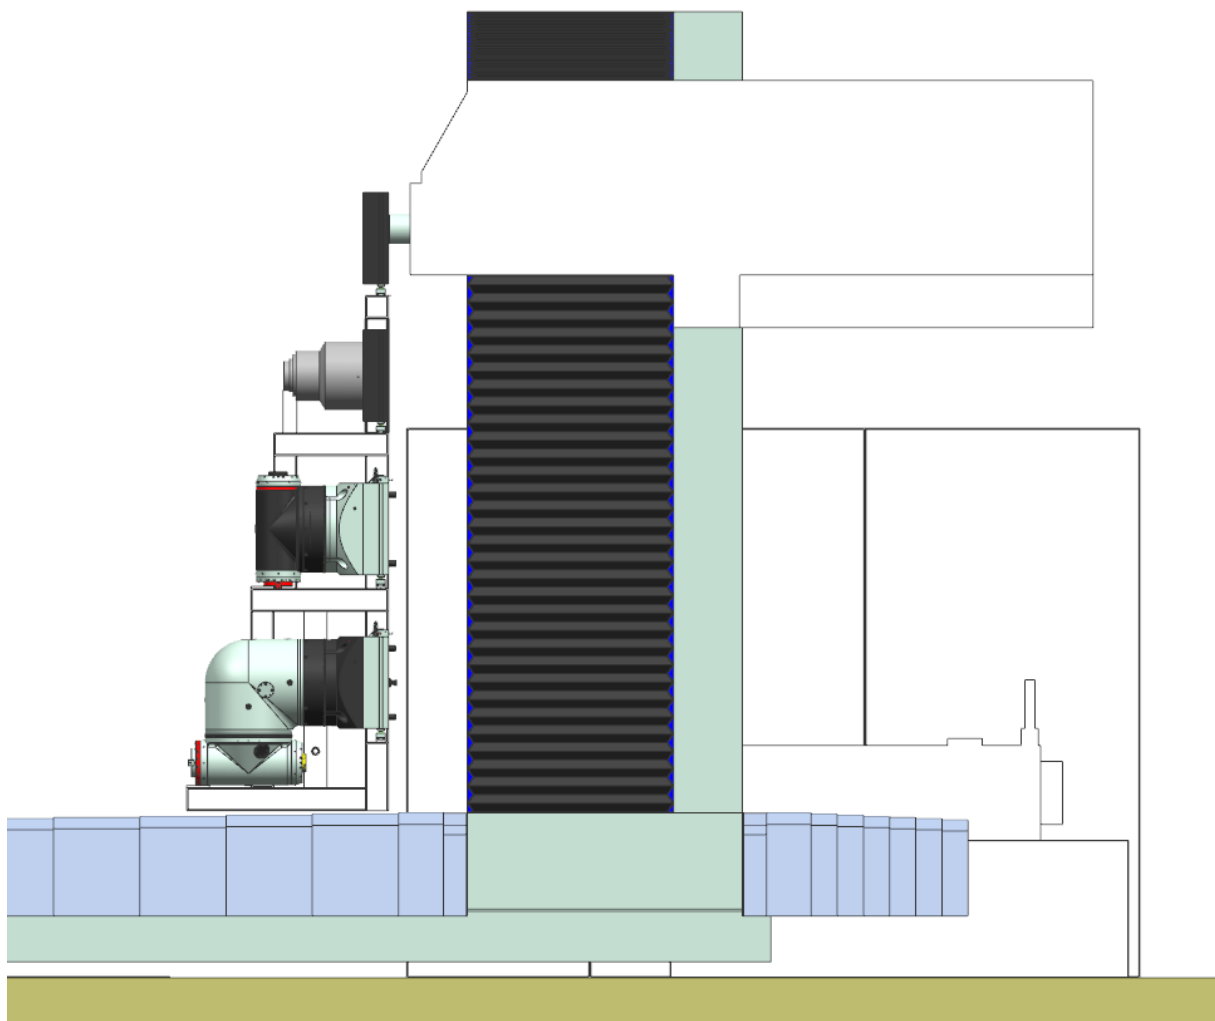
Svařovaná konstrukce zásobníku
